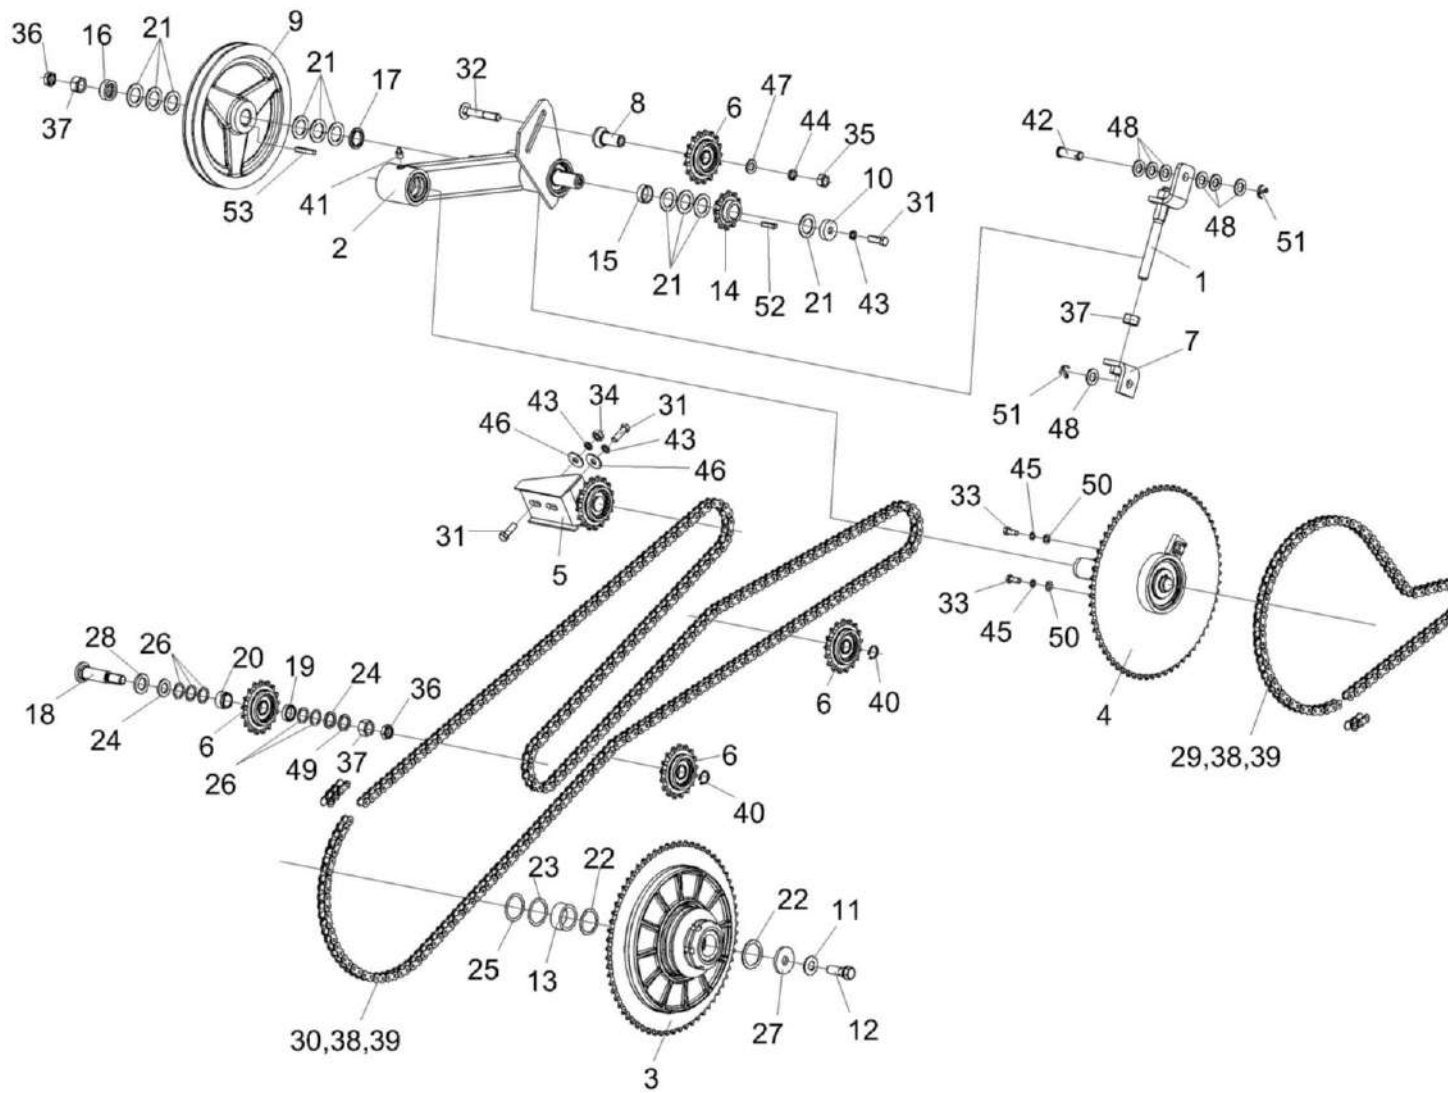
Установка привода мотовила ЖТ-9-1504500
